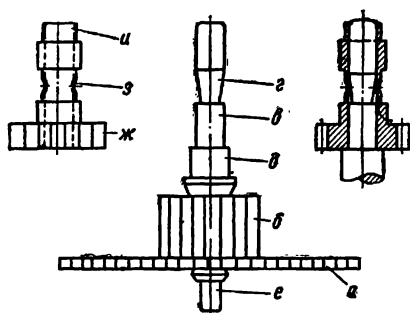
Минутный триб (закрепление триба на оси центрального колеса): а — центральное колесо; б — триб центрального колеса; в — ось триба центрального колеса; г — конусная выточка оси в; д, е, — цапфы триба центрального колеса; ж — минутный триб; з — уступ минутного триба; и — место посадки минутной стрелки
